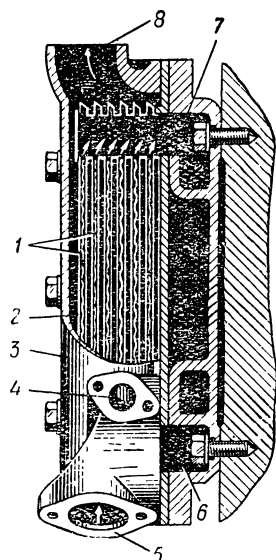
Масляный радиатор дизеля ЯАЗ-204: 1 — сердечники; 2 — трубка; 3 — корпус; 4 — входное масляное отверстие; 5 — входное водяное отверстие; 6 — нижний резервуар; 7 — верхний резервуар; 8 — верхний патрубок
